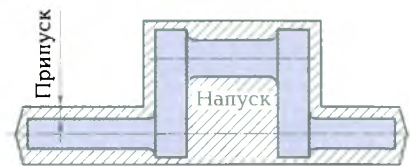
Заготовка коленчатого вала, выполненная с напуском
